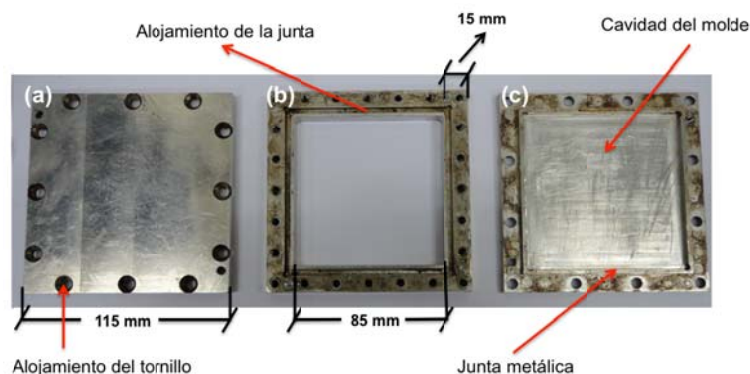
Molde de aluminio utilizado en la fabricación de los paneles de polipropileno. (a) Tapa superior. (b) Cuerpo del molde. (c) Tapa inferior.
